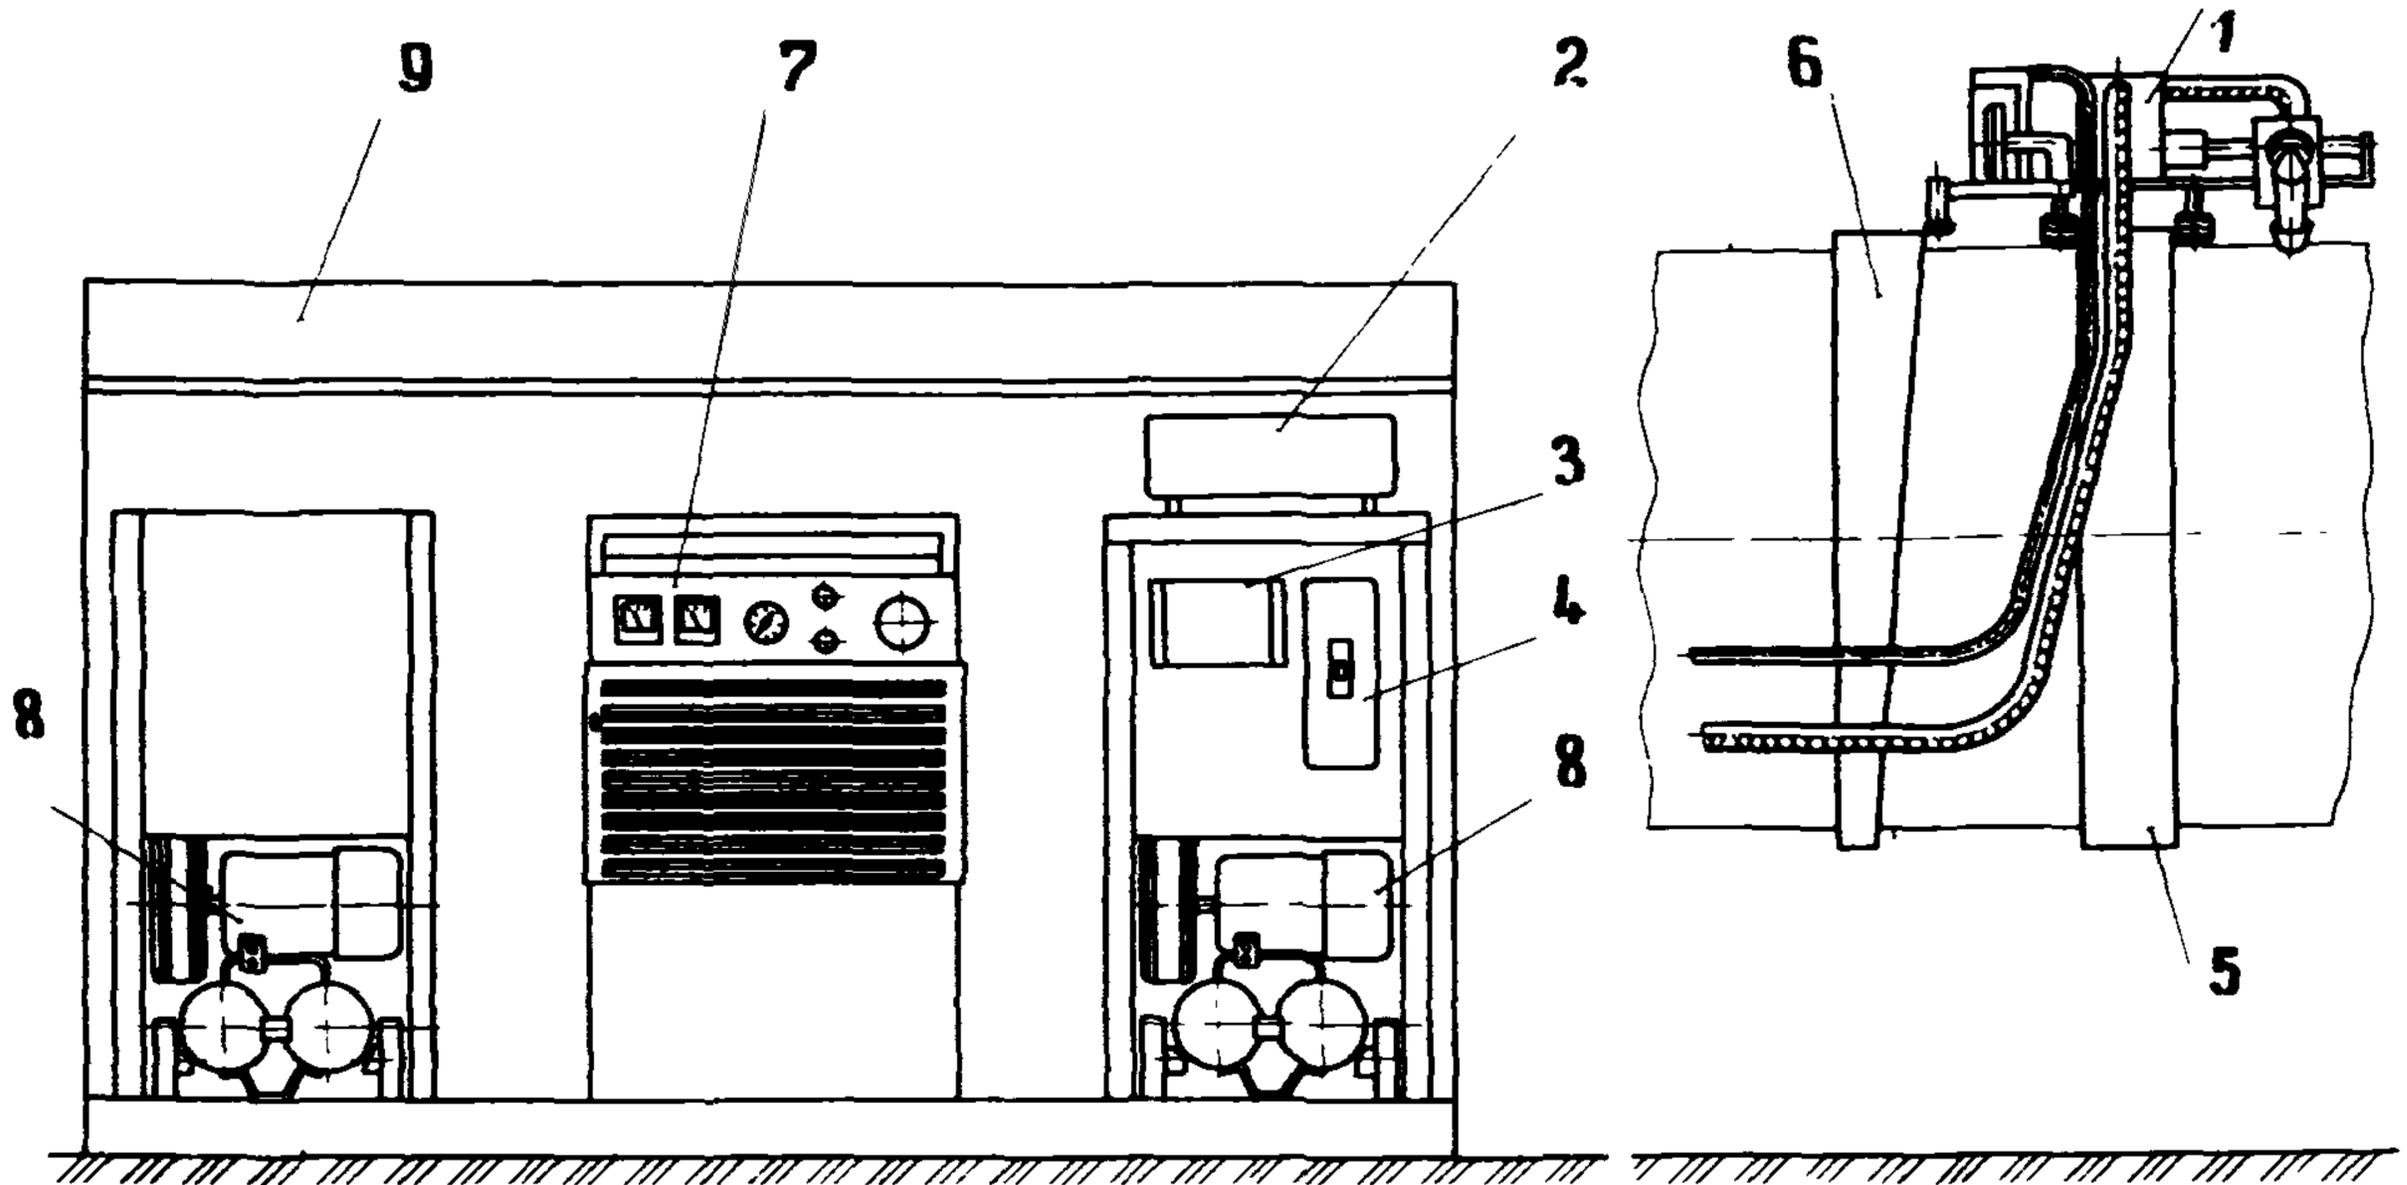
Схема установки "Орбита Пл-І" для воздушно-плазменной резки:
